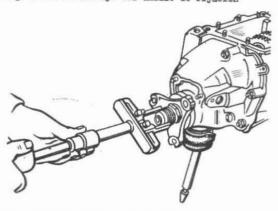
Desmontaje del anillo centrador del acoplamiento elástico del árbol cardánico empleando el expulsor A.40006/I y el extractor A.40005/4
